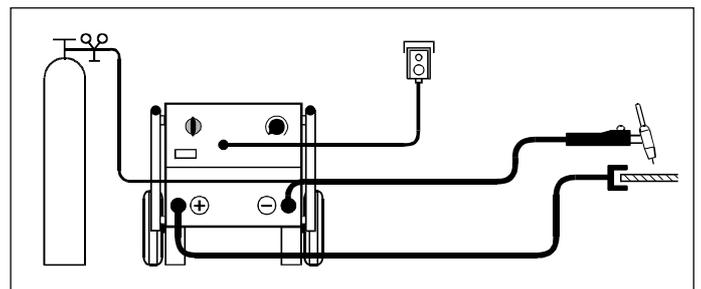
WTU en tant que source de courant du soudage TIG
